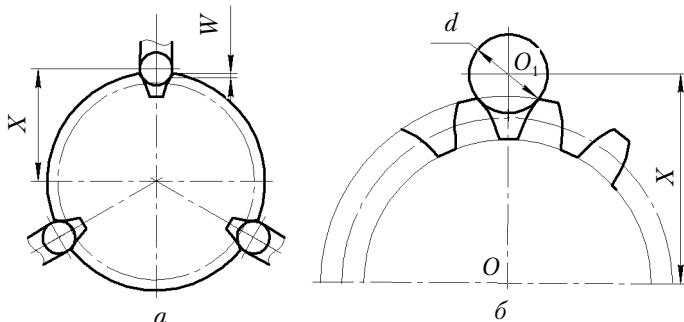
Схема центрирование зубчатого колеса по рабочим поверхностям зубьев
